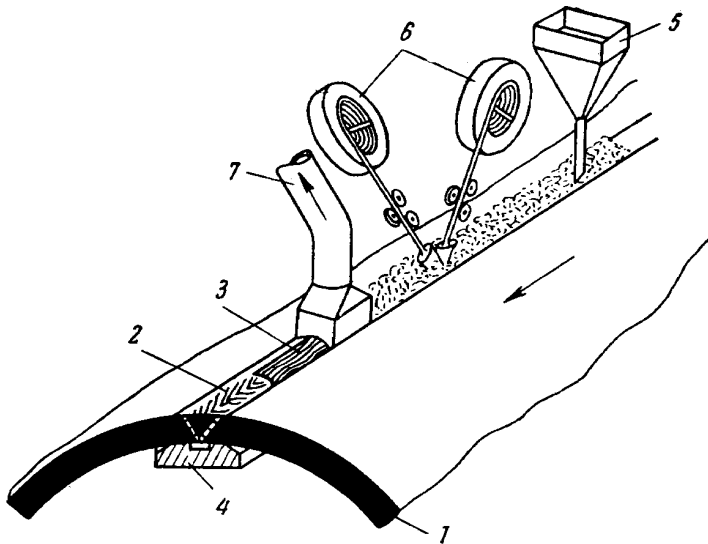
Схема сварки труб под слоем флюса:
